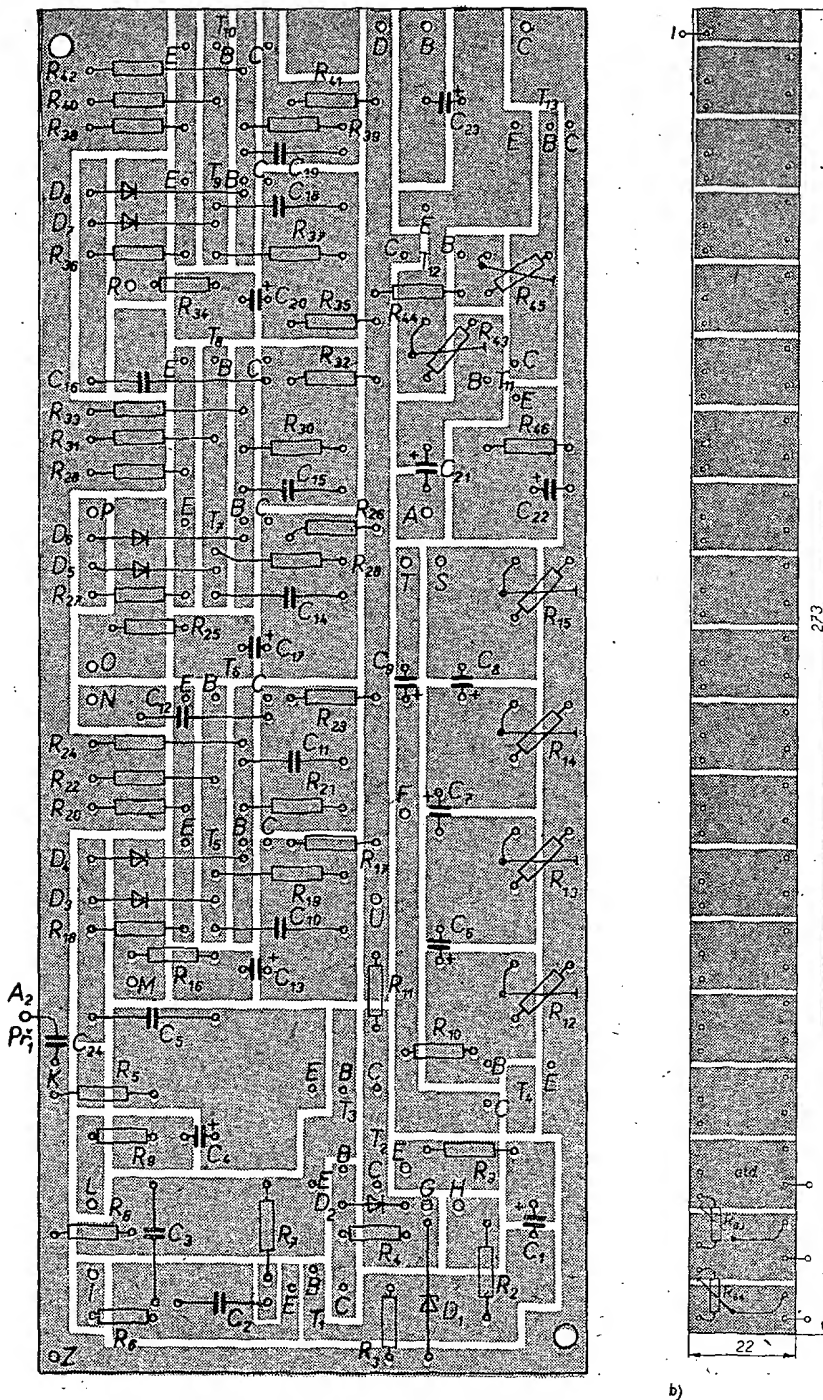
Možná zapojení vibrátoru a úprava desky s plošnými spoji
